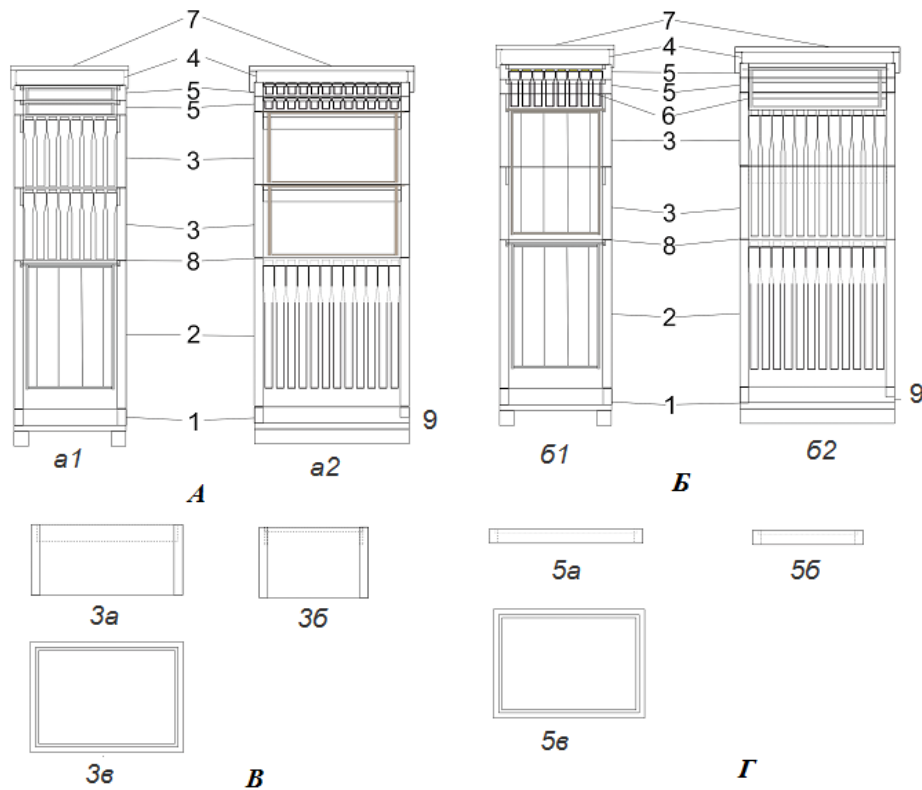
Уніфікований багатофункціональний вулик (А, Б – варіанти повної комплектації; а1, б1 – головний вигляд; а2, б2 – вигляд зліва; В – магазинний корпус; Г – мала надставка): 1 – дно; 2 – гніздовий корпус з 12 рамками розміром 300×435 мм; 3 – магазинний корпус; 3а – головний вигляд магазинного корпусу; 3б – вигляд зліва магазинного корпусу; 3в – вигляд зверху магазинного корпусу; 4 – утеплювач; 5 – мала надставка; 5а – головний вигляд малої надставки; 5б – вигляд зліва малої надставки; 5в – вигляд зверху малої надставки; 6 – вісім магазинних рамок розміром 435×230 мм; 7 – дах; 8 – розділювальна решітка; 9 – льоток
